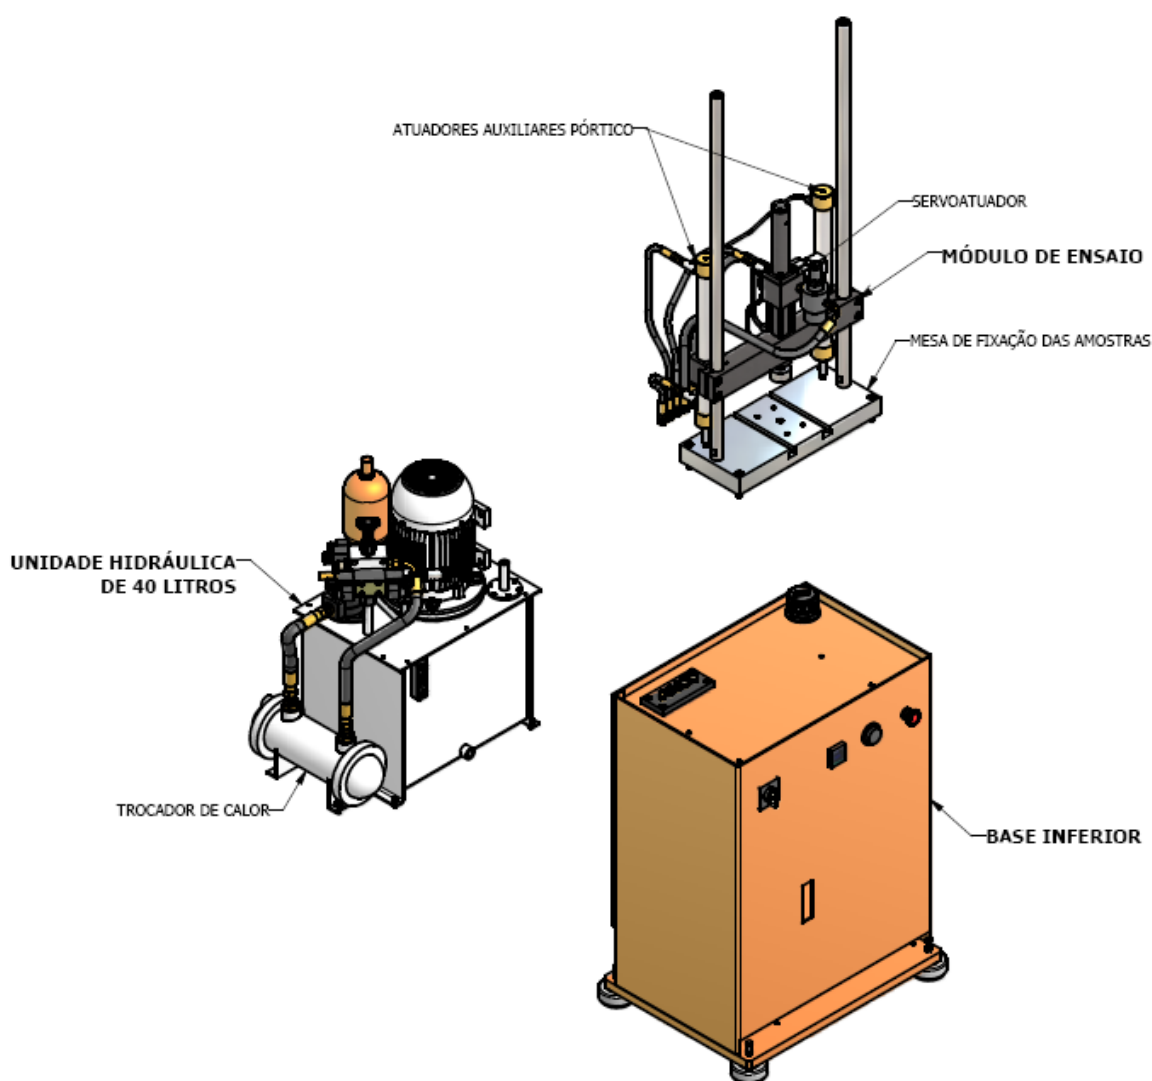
Vista em explosão da montagem da máquina de ensaios
